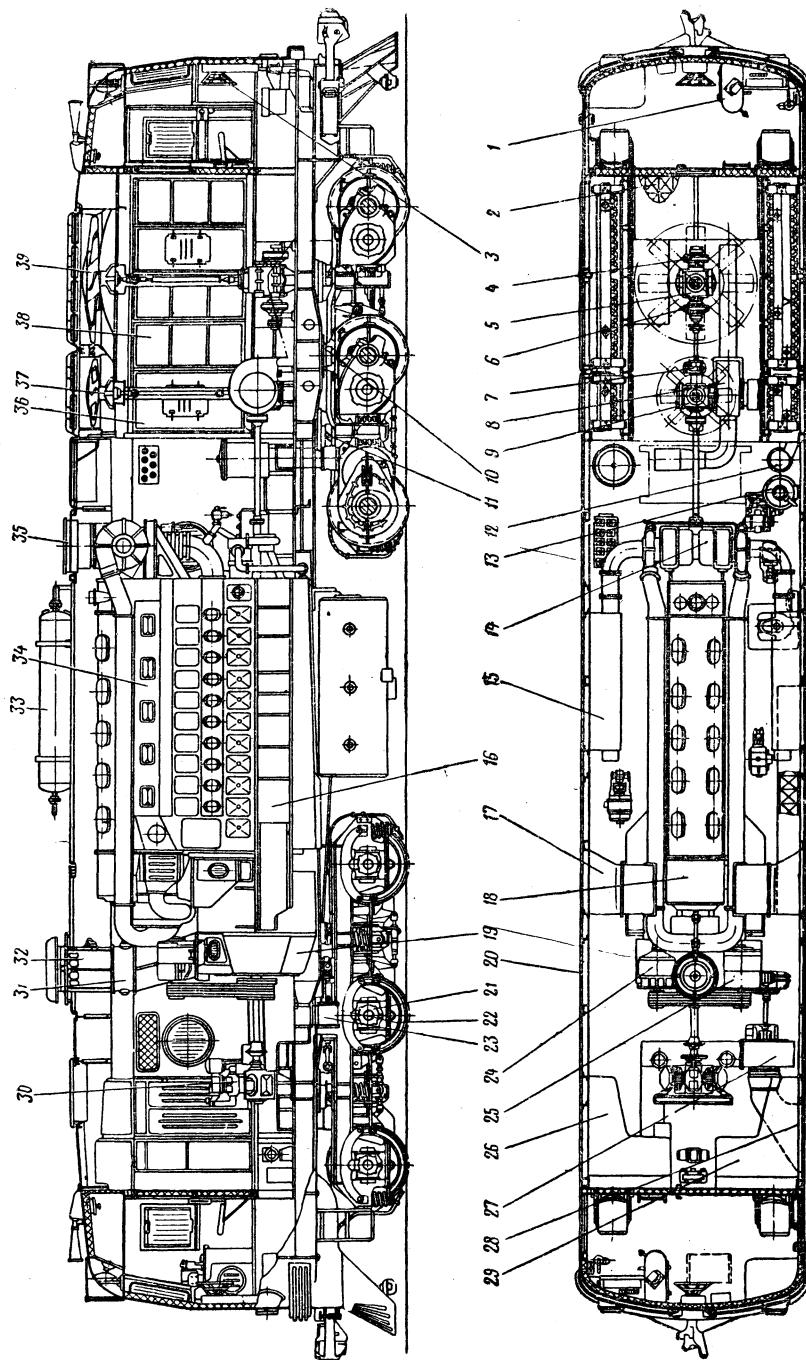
Продольный разрез и план тепловоза ТЭ10:
